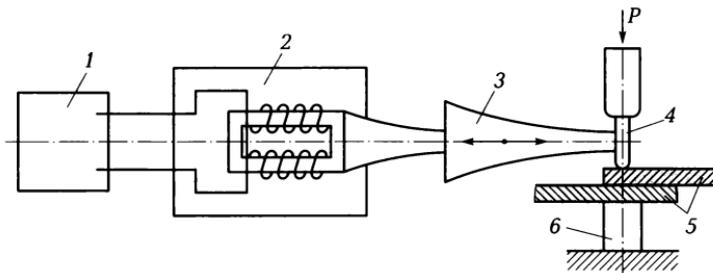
Схема точечной ультразвуковой сварки:
